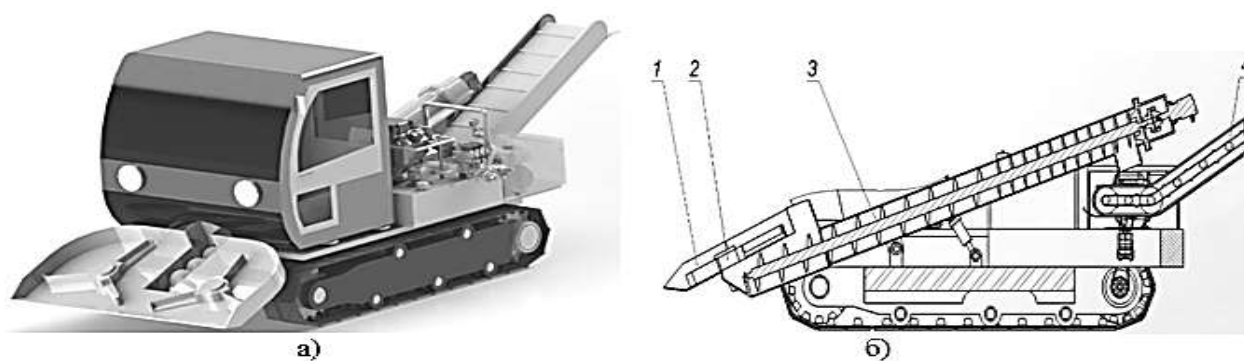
Внешний вид (а) и принципиальная схема механизмов снегоуборщика-(б): 1 – отвал; 2 – питатель лопастной; 3 – пресс шнековый; 4 – скребковый конвейер.
